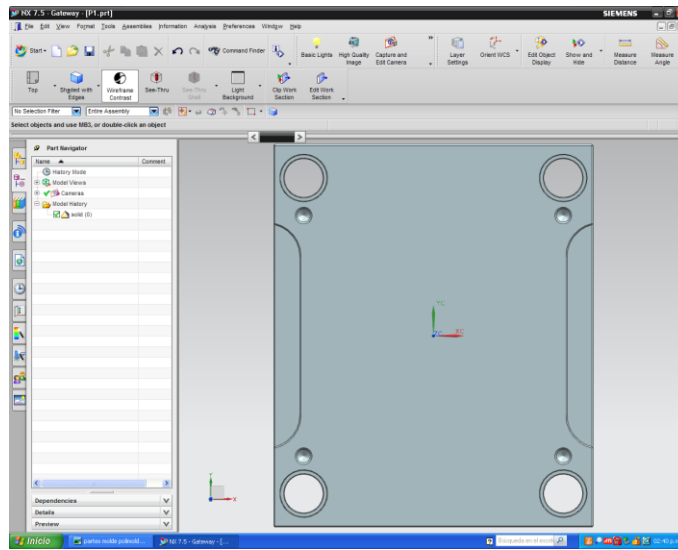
Placa frontal de cavidad P1, vista frontal.
